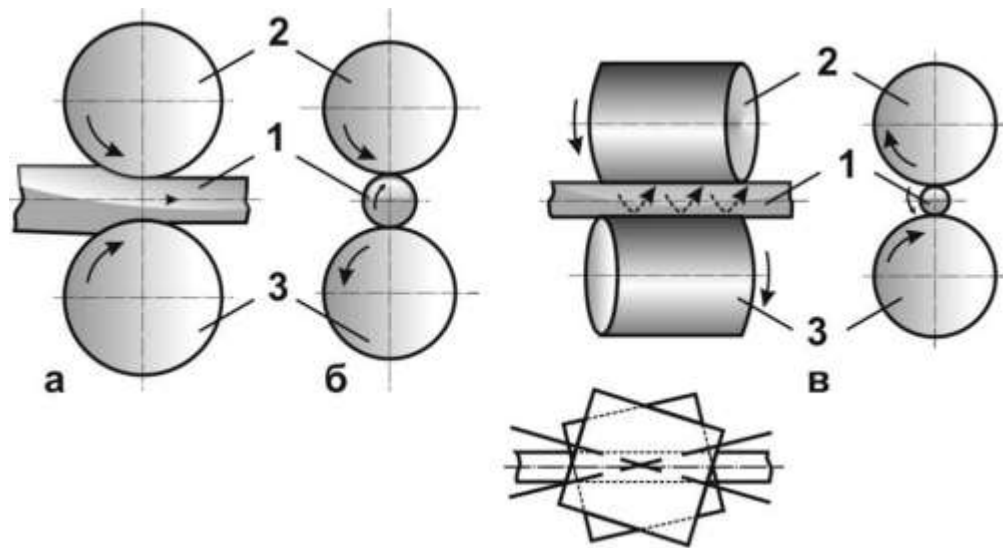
Види обробки металу методом прокатки: 1 – заготовка; 2,3 - валки.
